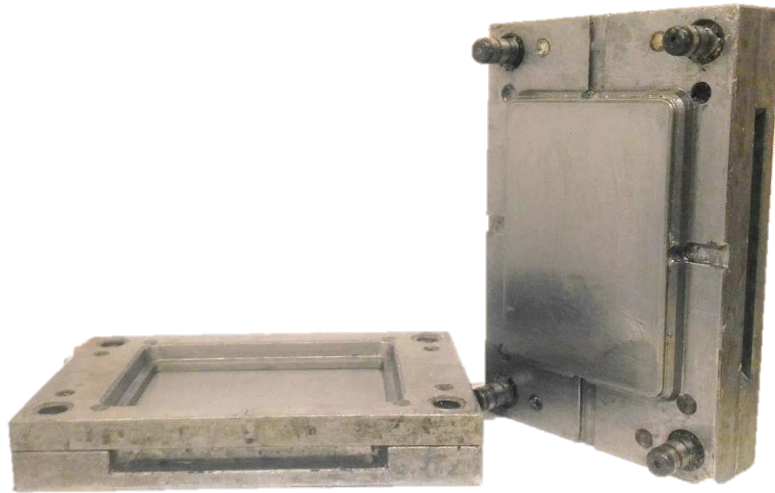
Molde utilizado no processo de moldação por deposição manual e compressão a frio.
